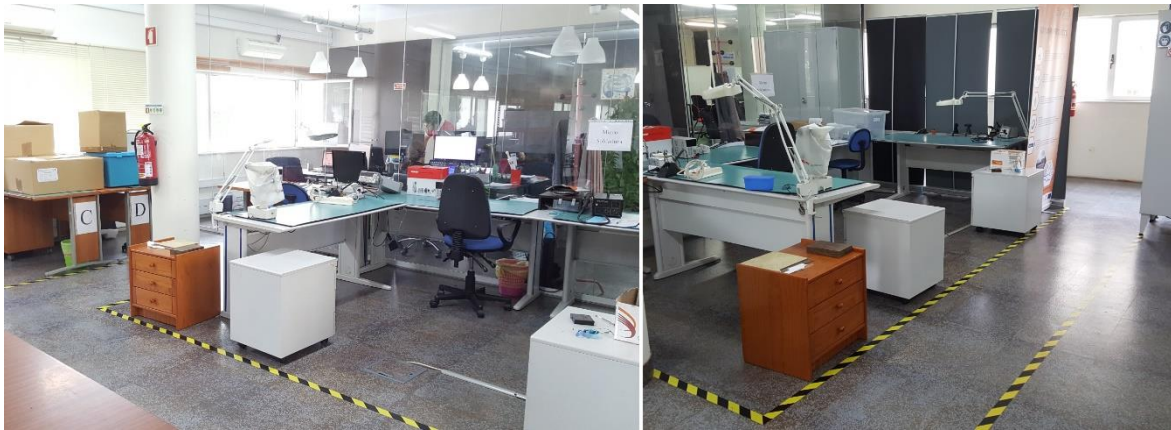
Área de microsoldaduras e testes de PCB's
